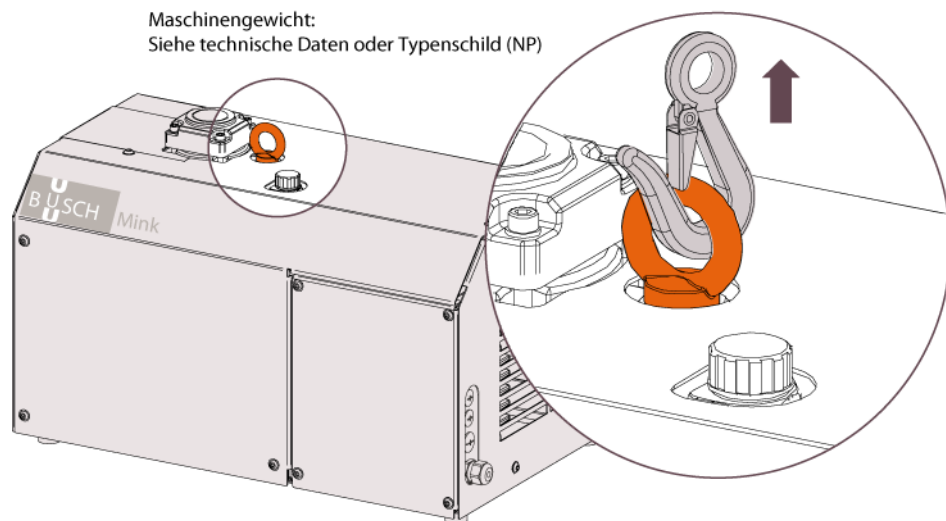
Transport der Vakuumpumpe an der Ringschraube
